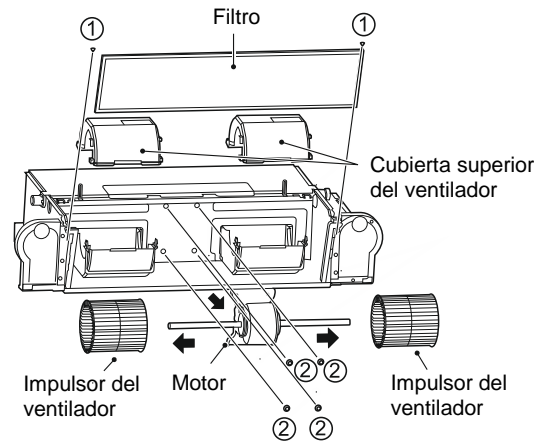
Desmontaje del filtro, de la cubierta superior del ventilador y del motor
